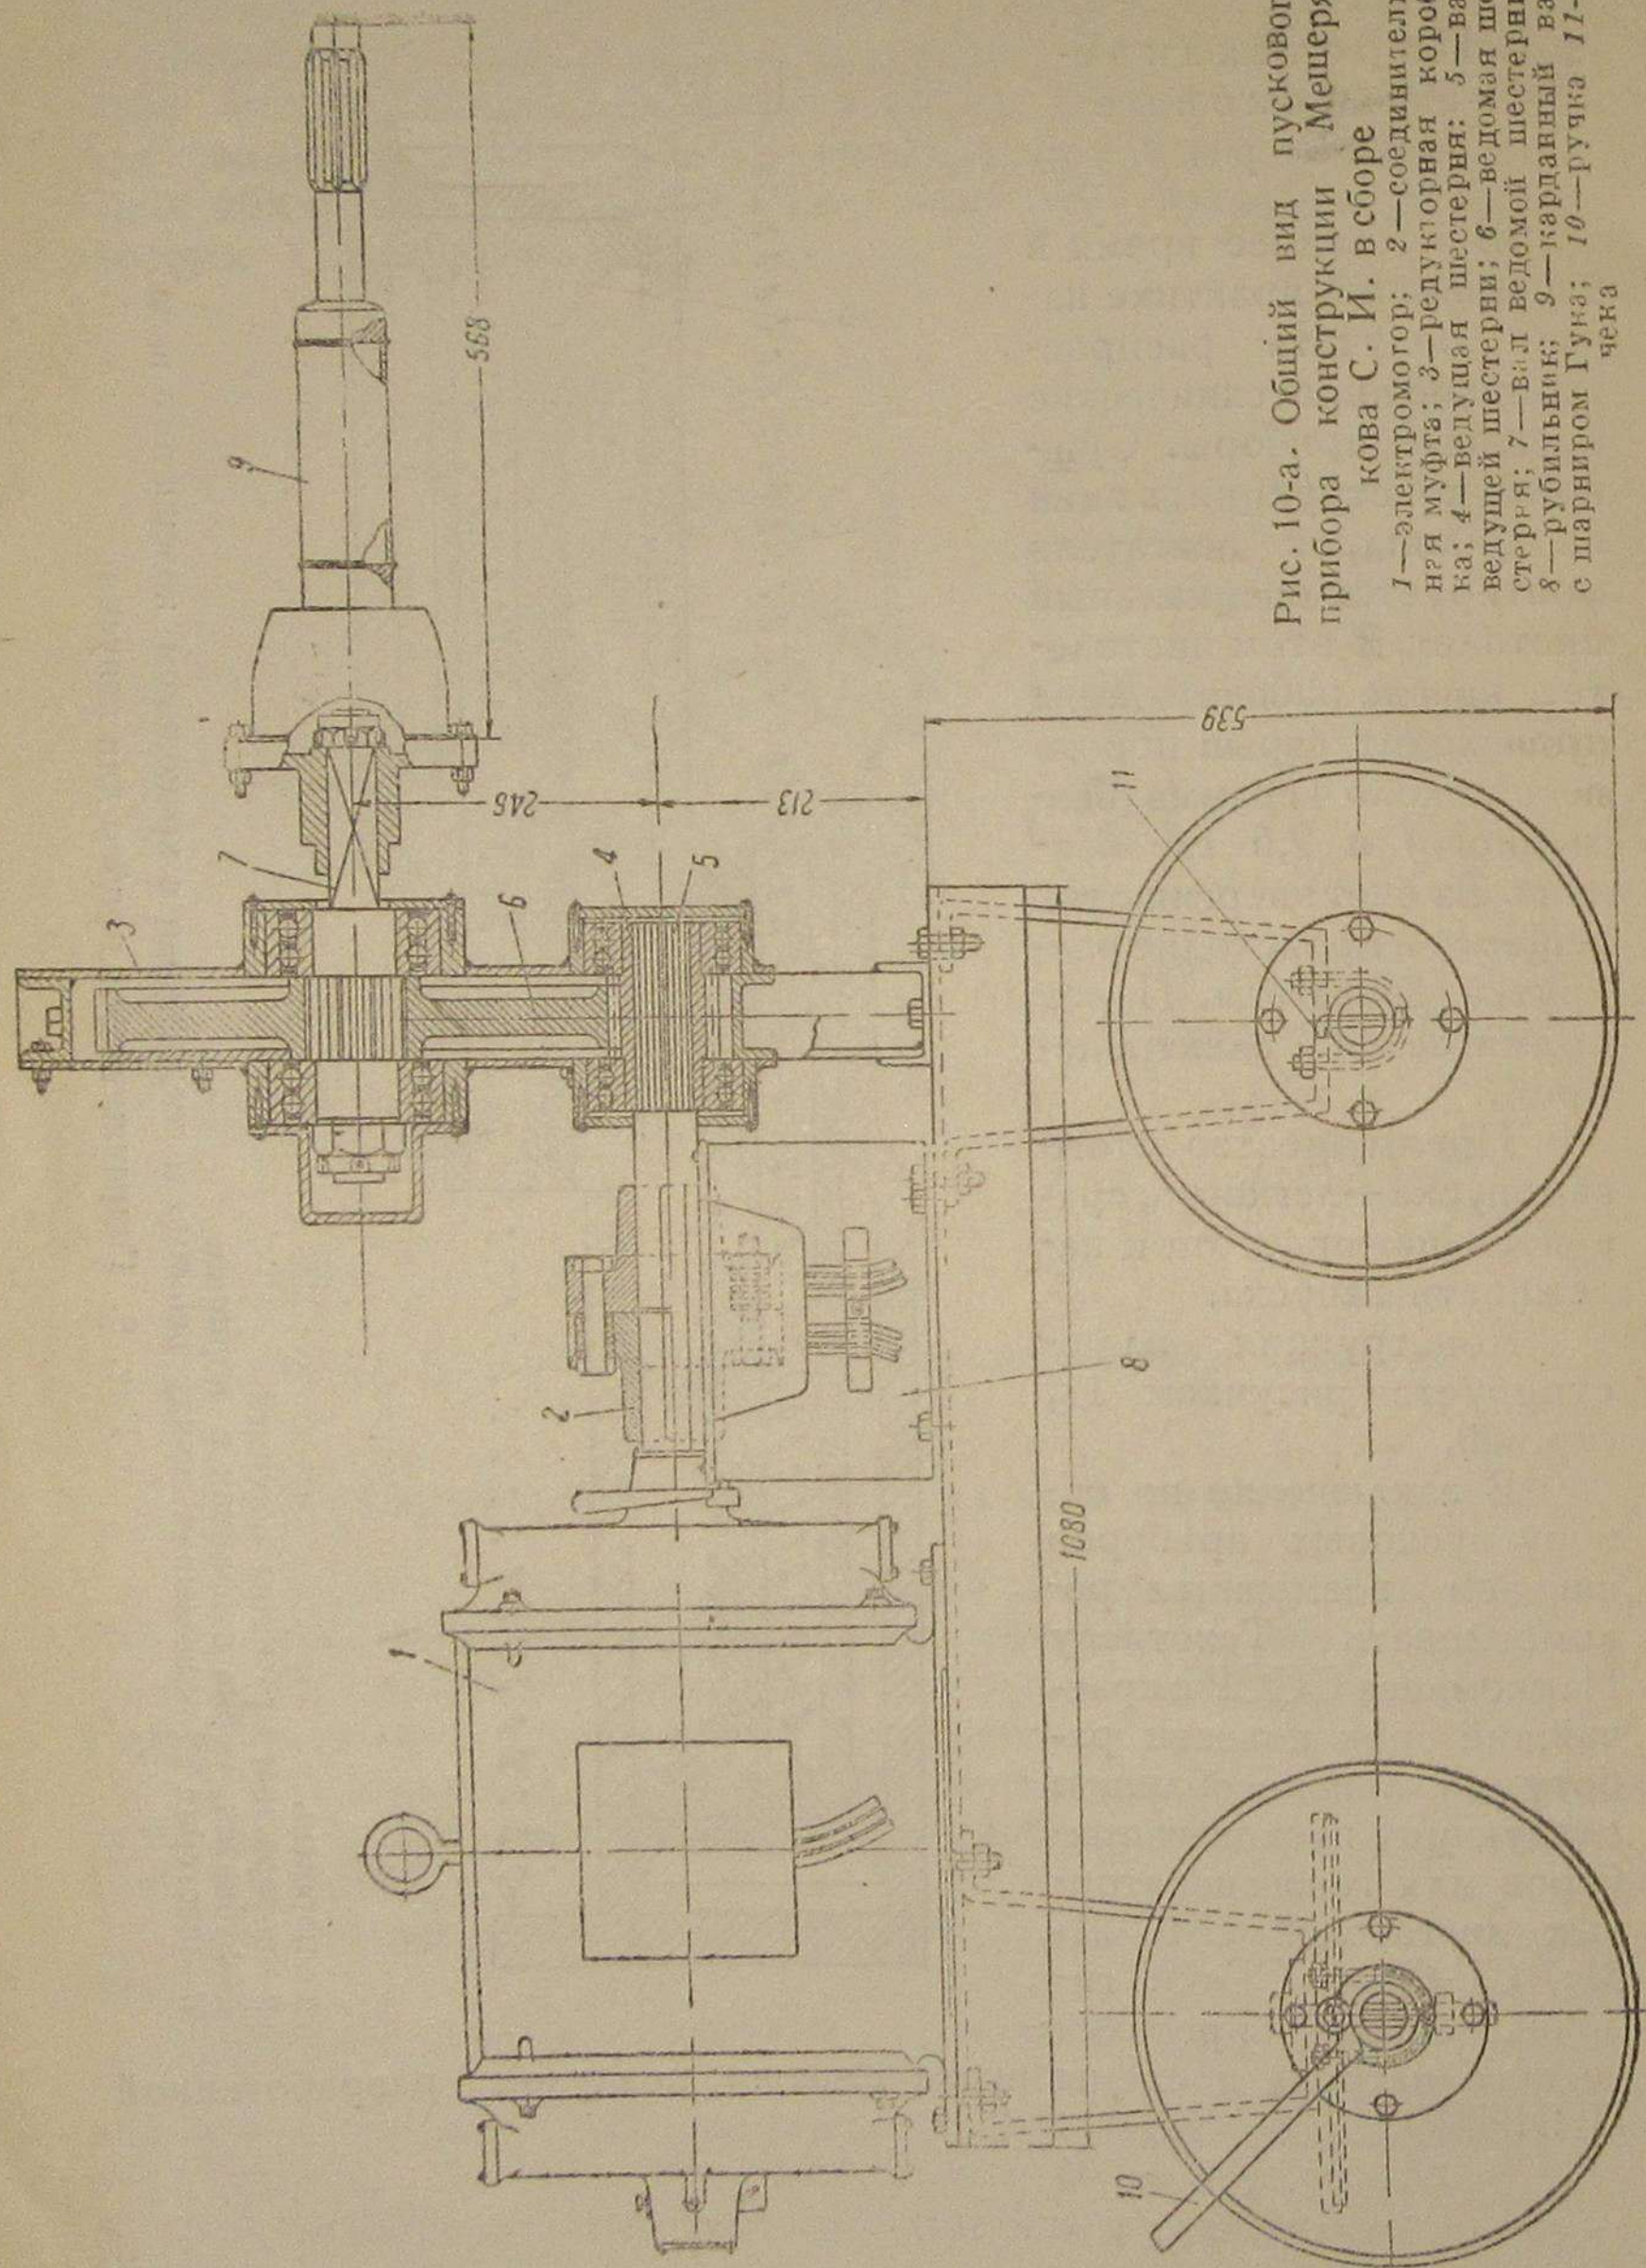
а. Общий вид пускового прибора конструкции Мешерякова С. И. в сборе
